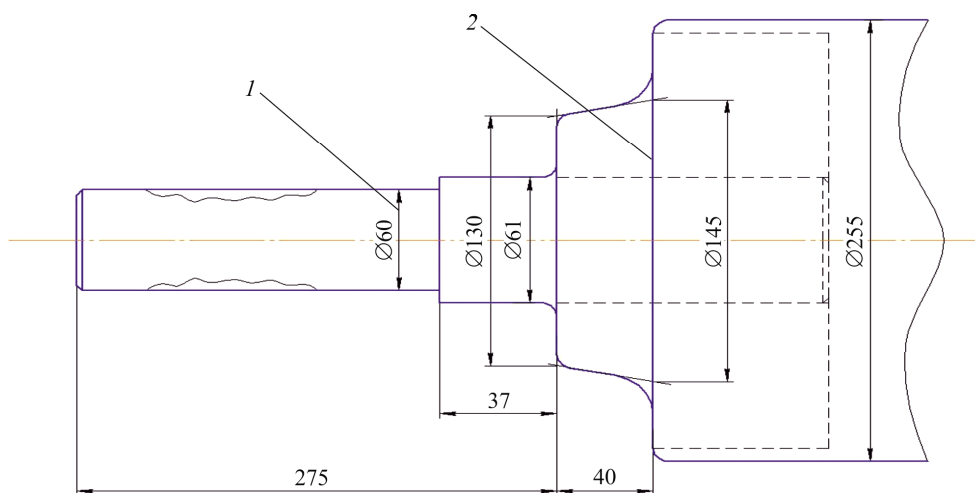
Фрагмент чертежа вала с цапфой: 1 – цапфа; 2 – вал
